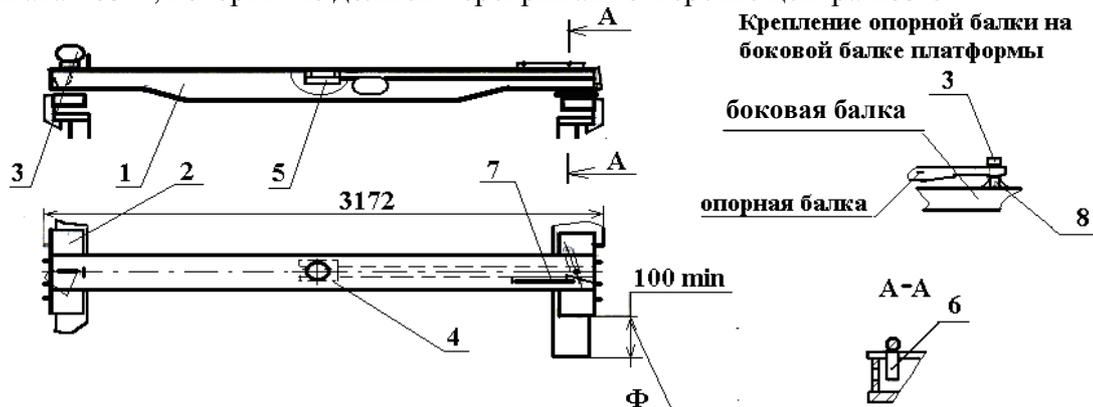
Опорная балка для крепления полуприцепа 1 – опорная балка; 2 – каретка; 3 – стопорная цапфа; 4 – захват; 5 – центр; 6 – фиксатор; 7 – рычаг; 8 – втулка
